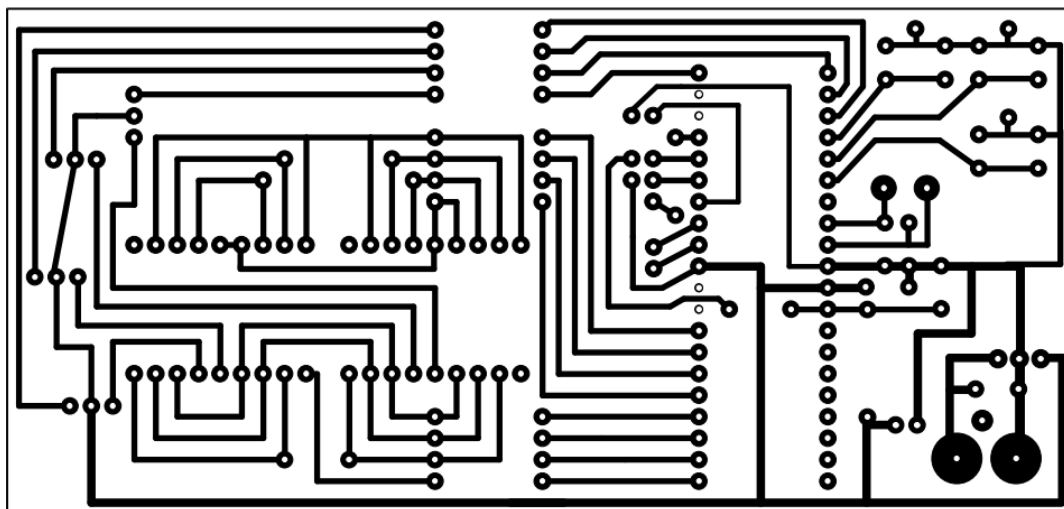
Внешний вид печатной платы (вид со стороны монтажа)
